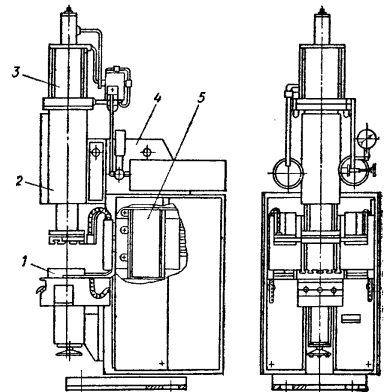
Машина МР-8001 для рельефной сварки
